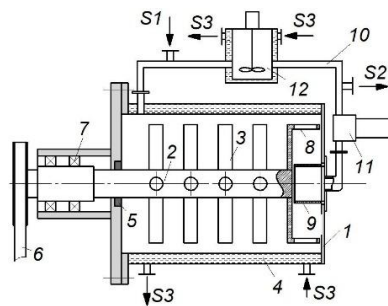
Бісерний млин, оснащений зовнішнім контуром циркуляції суспензії: 1 — стакан; 2 — ротор; 3 — робочі органи; 4 — охолоджувальна сорочка; 5 — ущільнення; 6 — привід; 7 — підшипниковий вузол; 8 — відцентровий сепаратор; 9 — патронний сепаратор; 10 — зовнішній контур циркуляції суспензії; 12 — охолоджувальна камера для суспензії. Патрубки: S1 — вводу суспензії; S2 — виходу суспензії; S3 — входу і виходу рідини у охолоджувальну сорочку
